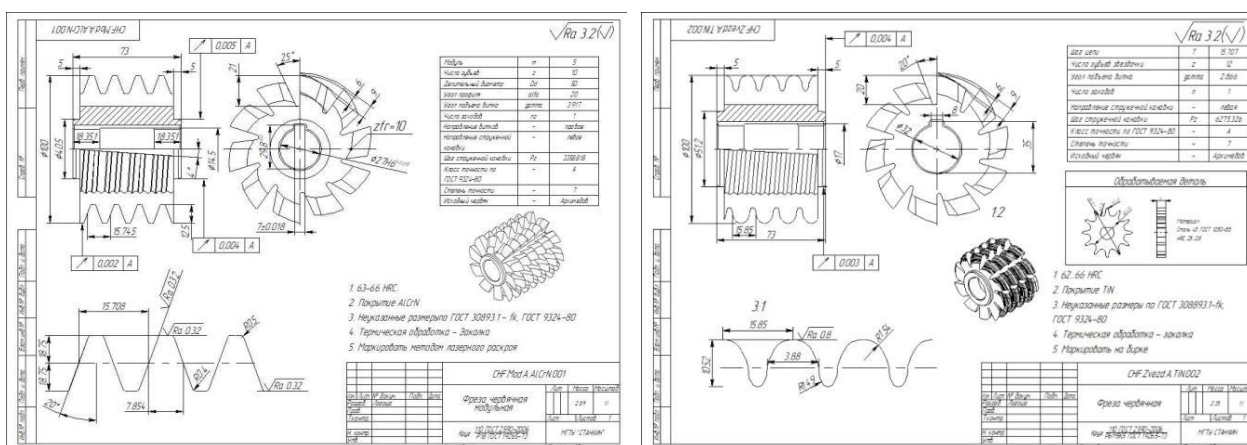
Параметрический чертеж червячной фрезы для эвольвентного колеса и для звездочки цепного привода
